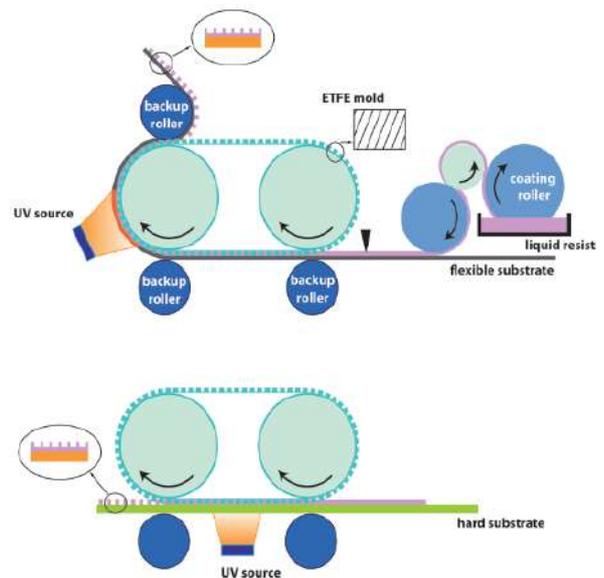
Roll-to-roll 그라비아 인쇄법(위)과 roll-to-plate 그라비아 인쇄법(아래).
